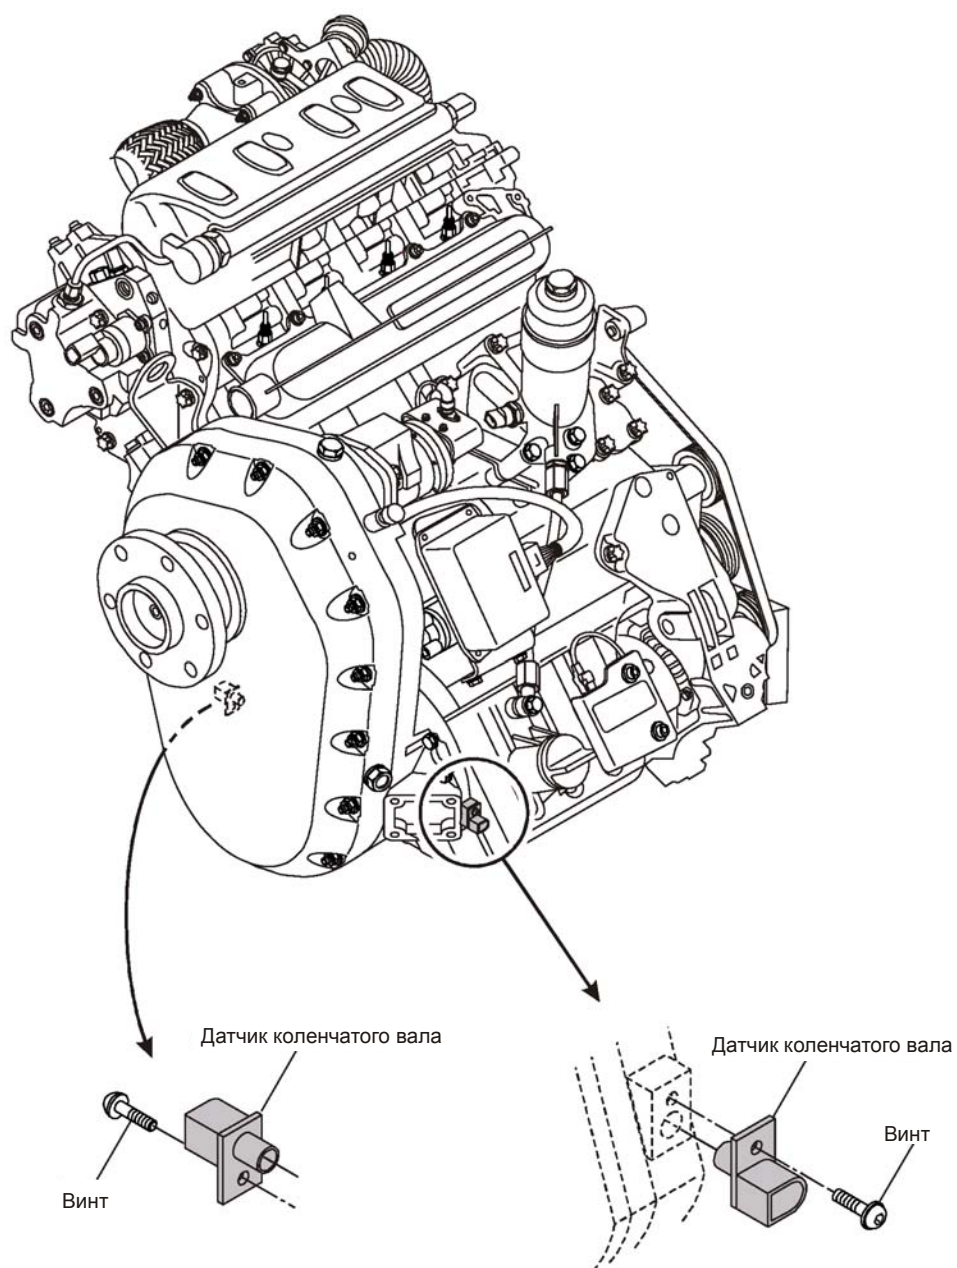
Установка датчика частоты вращения коленчатого вала (оборотов двигателя)
